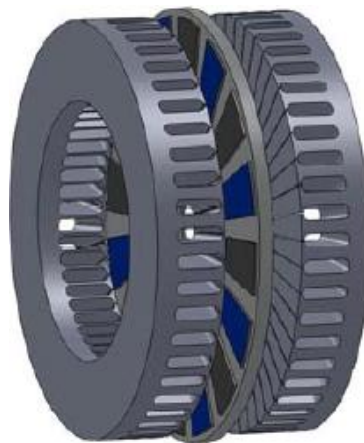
GSIP de fluxo axial, de rotor circular simples [36].
